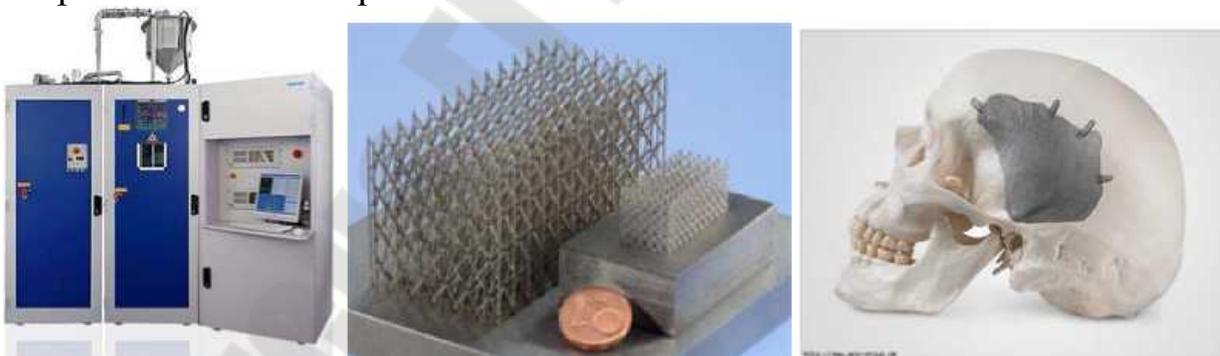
АФ машина Realiser SLM 250 и образцы изделий из титана.
